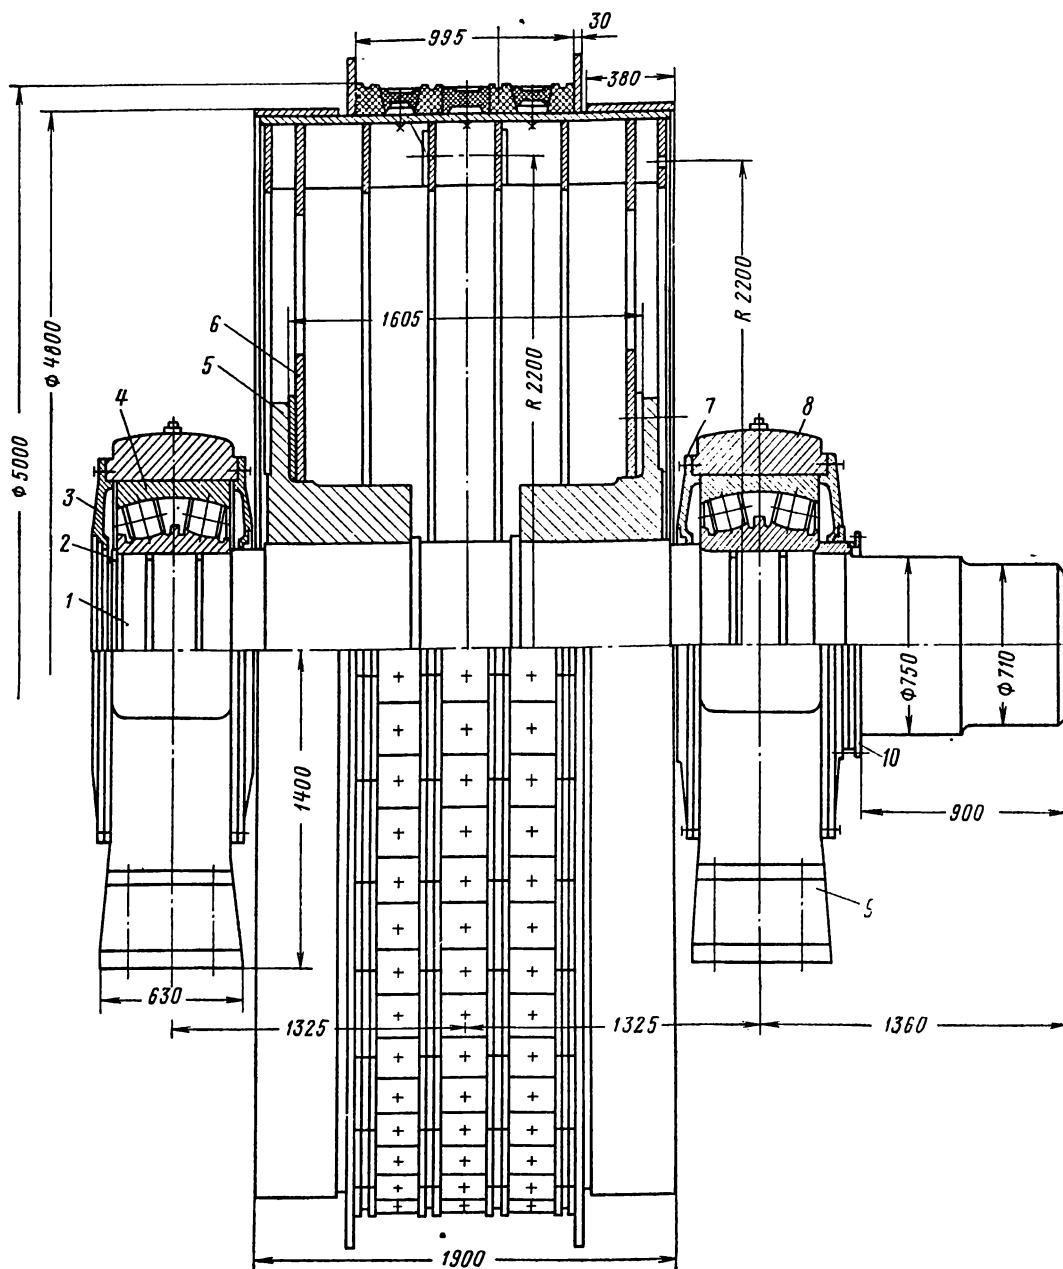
Сборка главного вала машины ЦШ5×4
